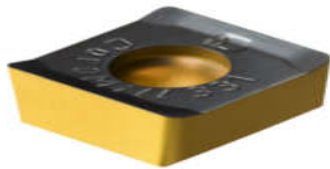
пластина дискової фрези N331.1A-04 35 05H-PL4340
